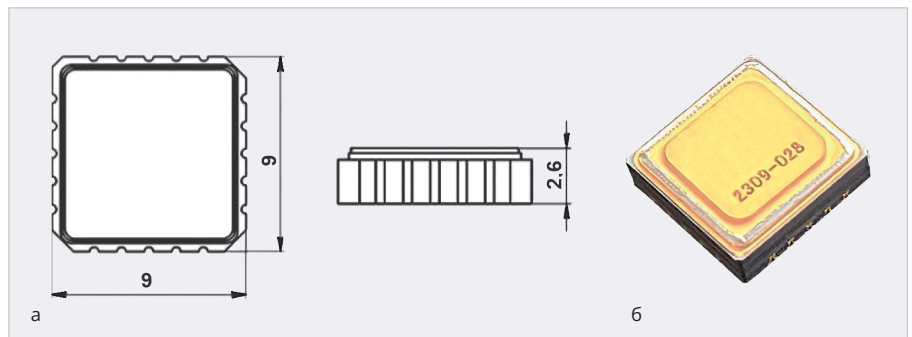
ИМС акселерометров: а) габаритные размеры; б) внешний вид
